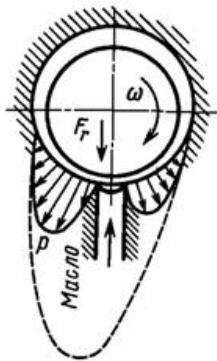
Гидростатическая смазка подшипника скольжения
